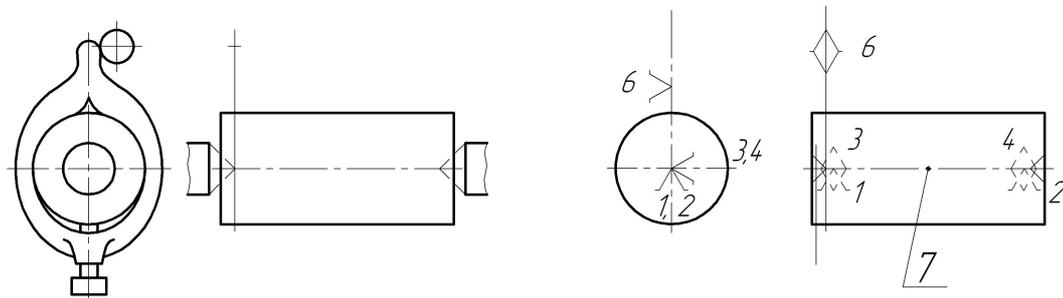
Установка вала в центрах: 1 – 6 – опорные точки;
